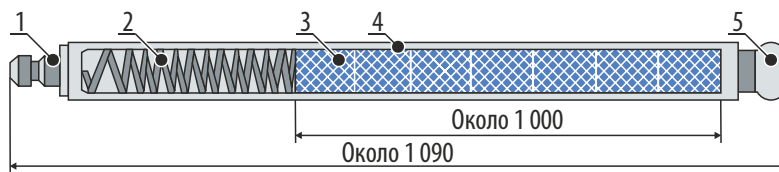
Конструктивная схема экспериментального твэла: 1 — верхняя заглушка, 2 — пружина, 3 — топливный сердечник, 4 — оболочка, 5 — нижняя заглушка
